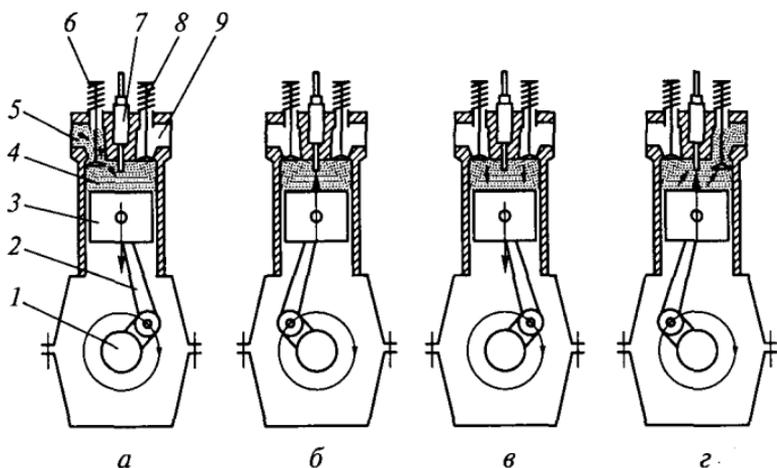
Схема рабочего цикла четырехтактного карбюраторного двигателя:
